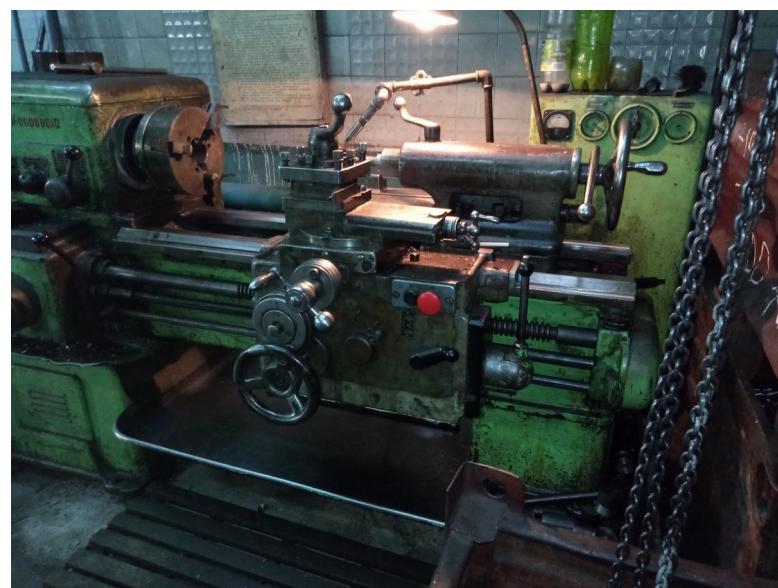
Токарно-винторезный универсальный станок 1К625
